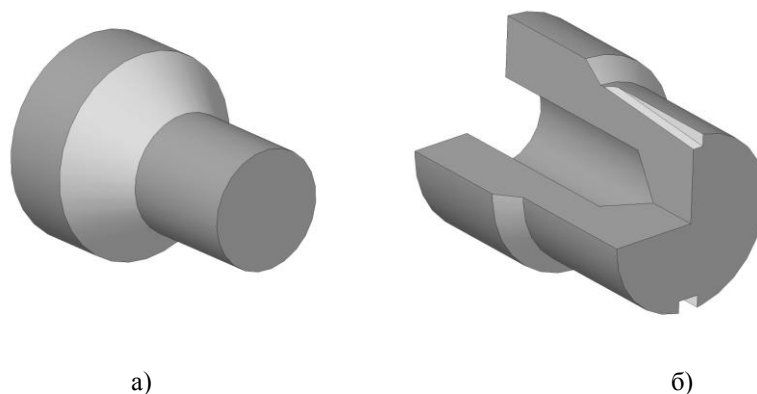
Конструкції золотників гальмівних клапанів: а – із конічною робочою поверхнею та б – поєднання конічної робочої поверхні з двома пазами
